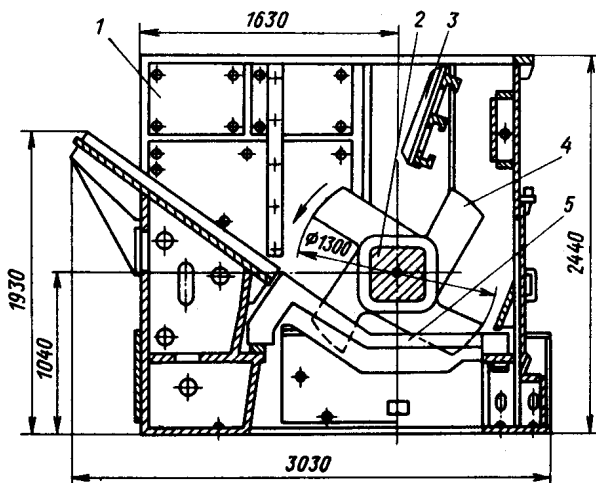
Одновалковая зубчатая дробилка: 1 – корпус; 2 – вал; 3 – отбойная плита; 4 – зубчатый венец; 5 – колосники.
